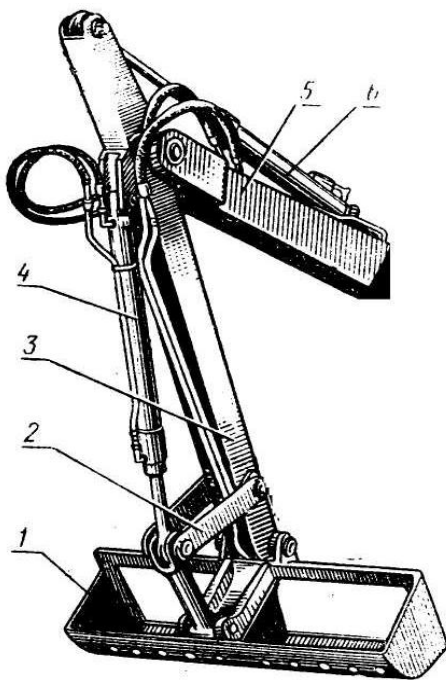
Общий вид поворотного ковша с перегородкой.
